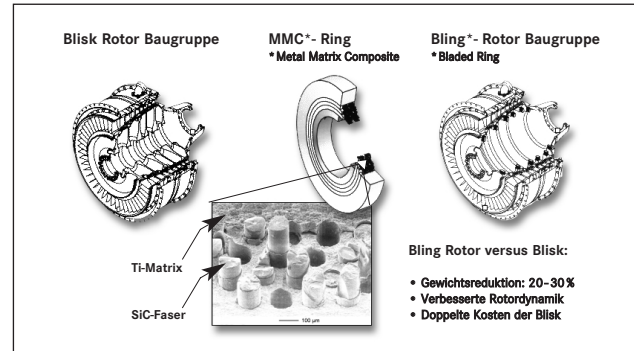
Hochdruckrotor in integraler Scheibe-Schaufel und integraler Ring-Schaufel-Bauweise
